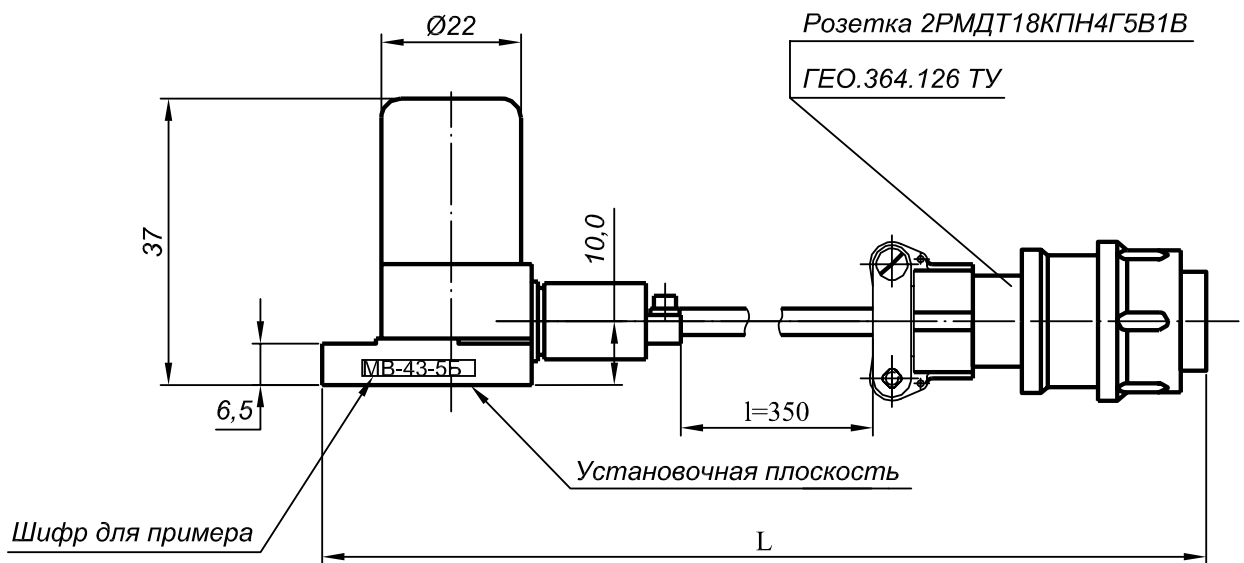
Габаритно-установочные размеры ВИП МВ-43-5Б/0,35
